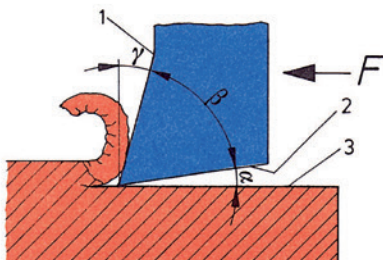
/9: Winkel und Flächen an der Werkzeugschneide und am Werkstück
